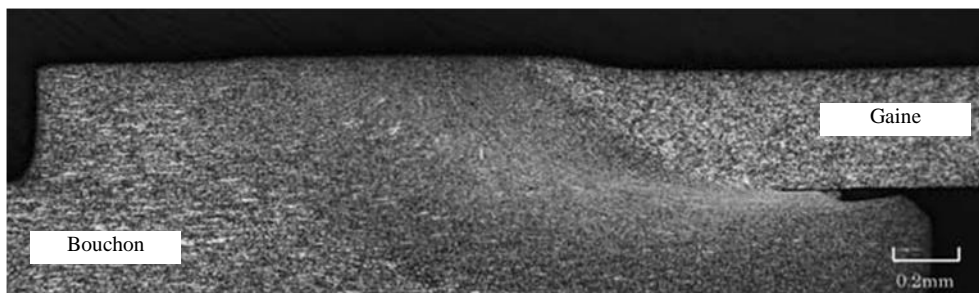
Macrographie de soudage d'un acier 9%Cr ODS [78]
